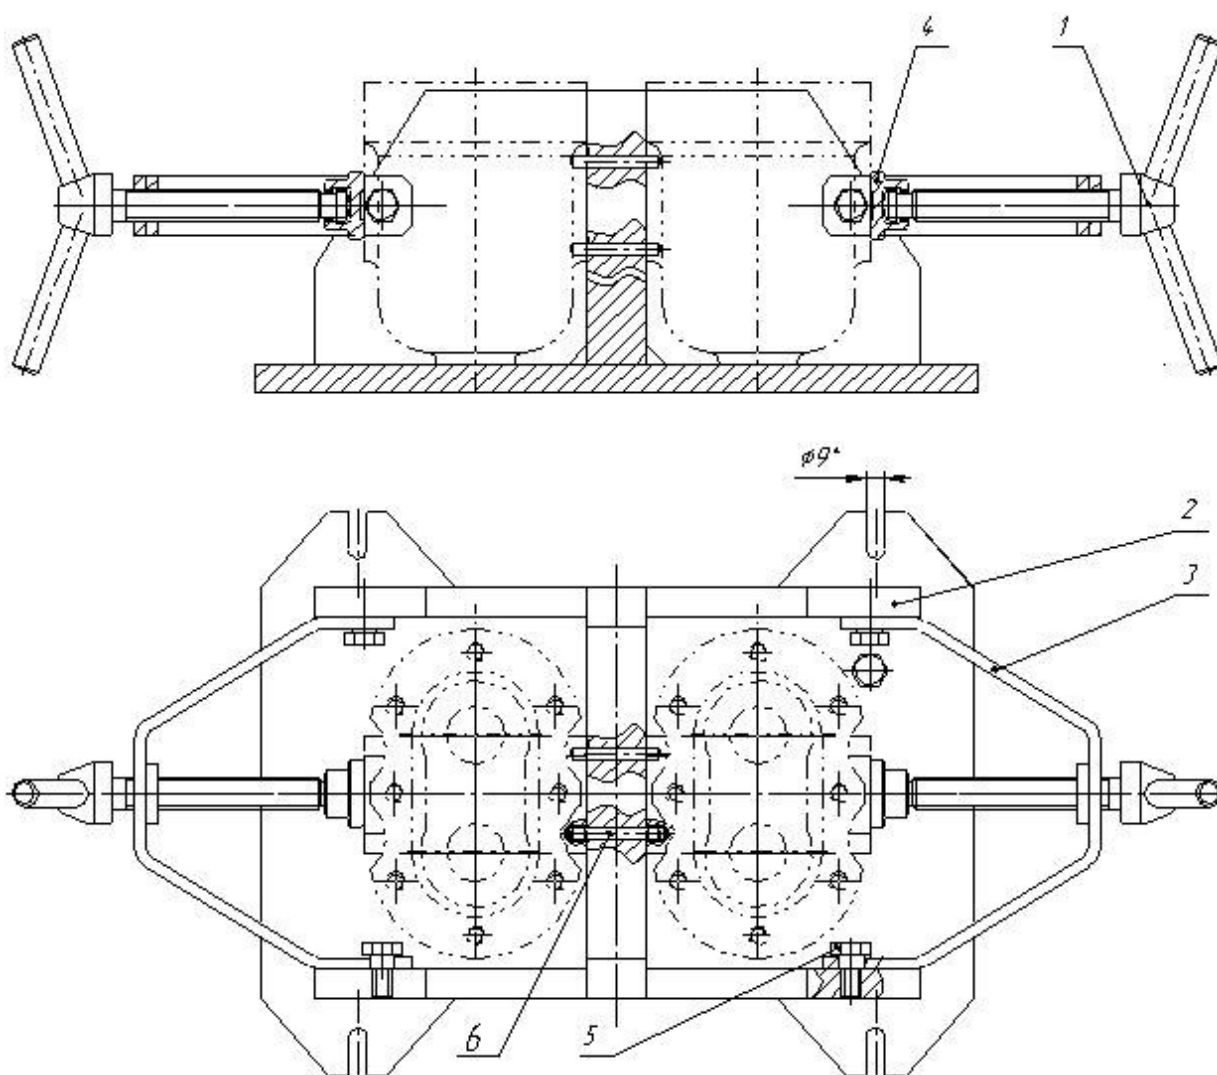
Приспособление для обработки корпуса насоса гидросистемы
